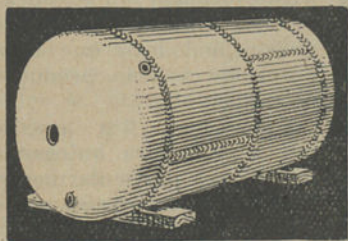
Grande reservatorio de aço macio construido por soldadura autogenea.
